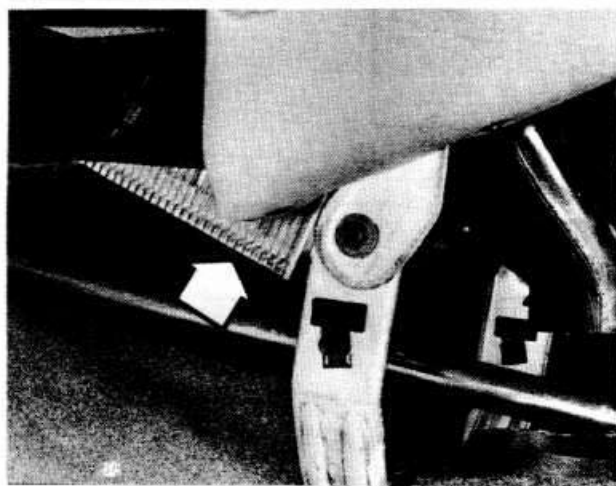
Вытащите сердцевину нагревателя из кожуха
